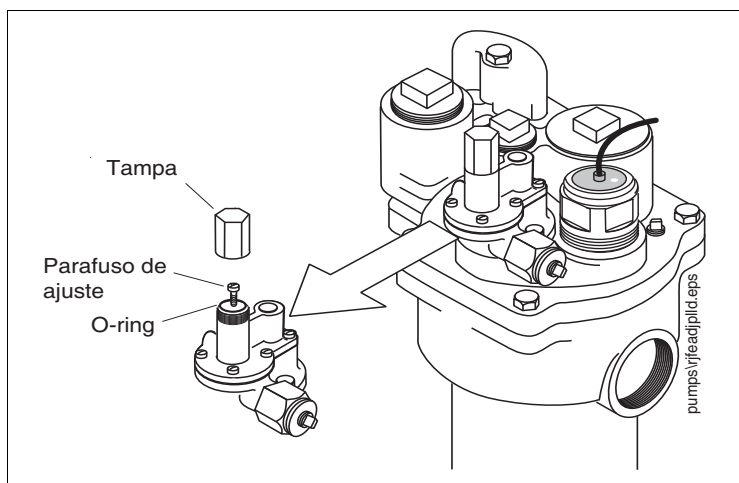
Conjunto de válvula ajustável ao pressostato (bomba padrão Red Jacket exibida)
